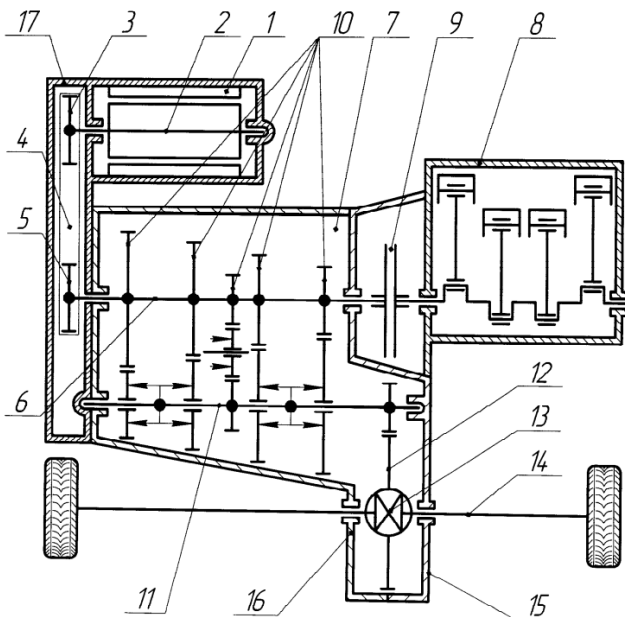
Схема ГСУ з пасовою передачею: 1 – електродвигун; 2 – вал електродвигуна; 3, 5 – шків; 4 – пас; 6 – вал коробки передач; 7 – коробка передач; 8 – ДВЗ; 9 – муфта зчеплення; 10 – зубчаста передача; 11 – вторинний вал коробки передач; 12 – головна передача; 13 – диференціал; 14 – ведуча ось; 15, 16 – половини корпусу; 17 – єдиний модуль
